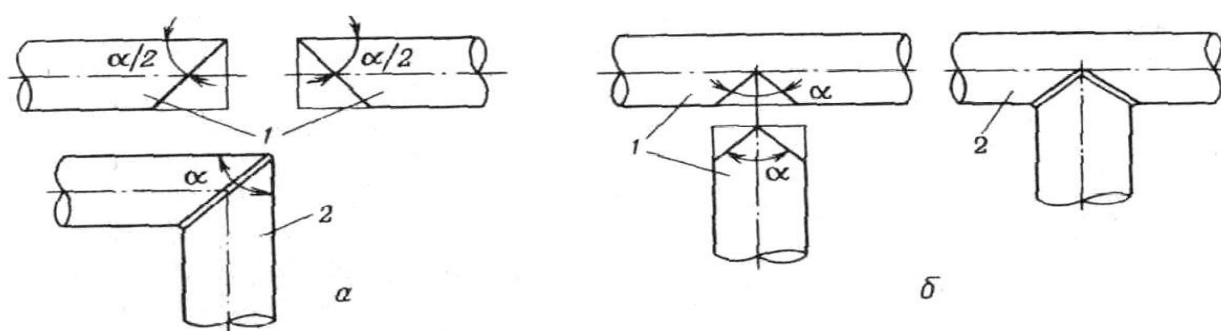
Сварка труб при угловом соединении: (а) и при изготовлении отводов (б): 1 – свариваемые детали; 2 – готовые изделия
